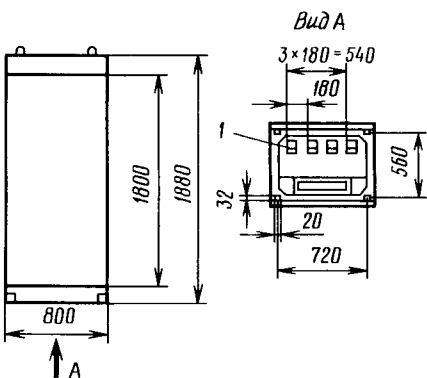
Габаритные размеры шкафа ПУ комплекса ТК-132:
